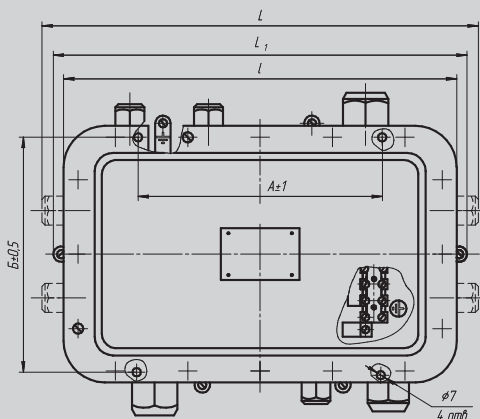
Коробки с привертными сальниками (пластмассовый)
